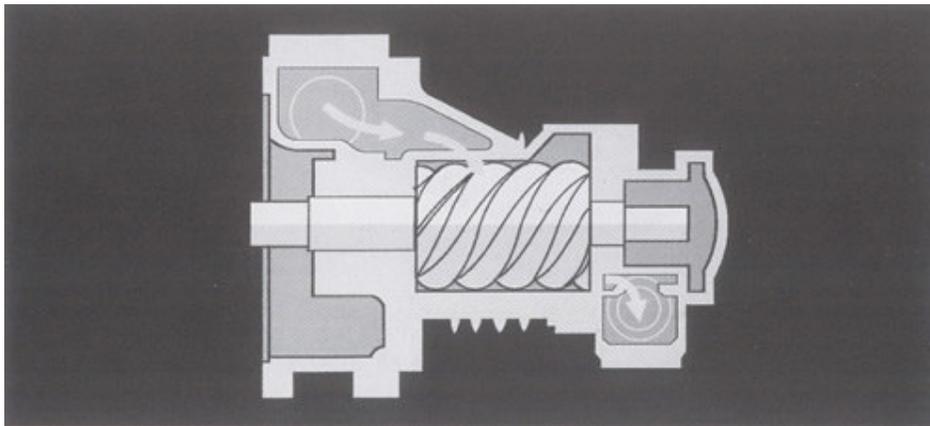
Esquema de compresor de simple tornillo rotativo.
